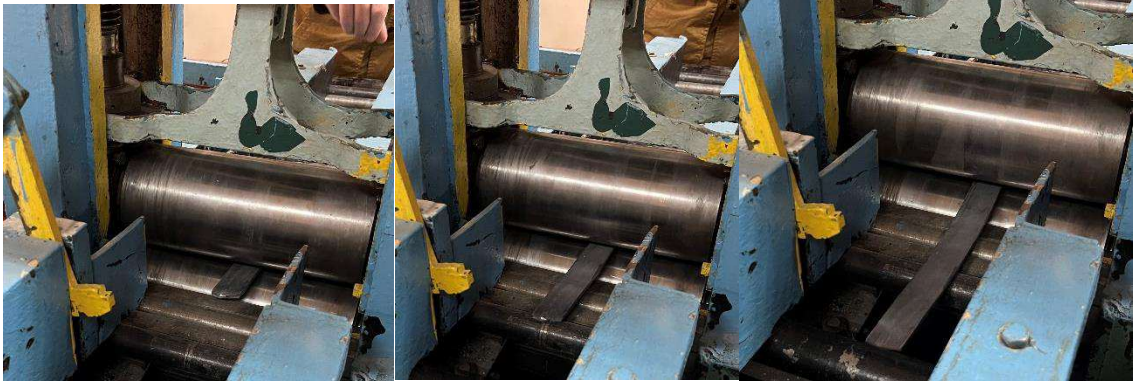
Прокатка свинцевої заготовки на лабораторному стані
